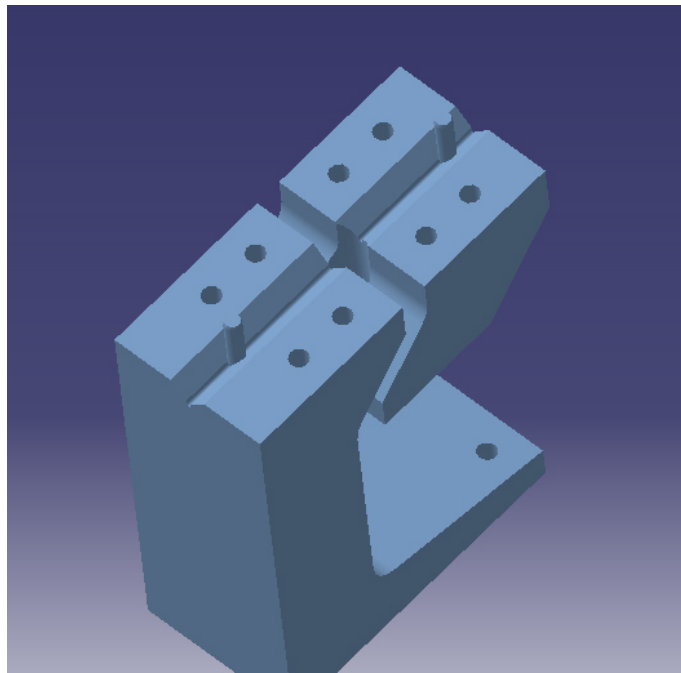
Detalle del rail existente en las cogidas para el posicionado de la probeta
